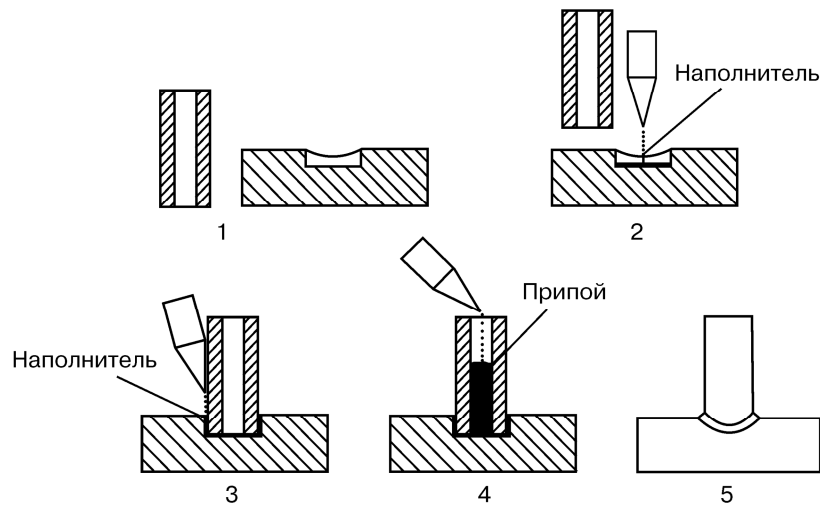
Схема зборки деталей для паяння при широкому зазорі з порошком
